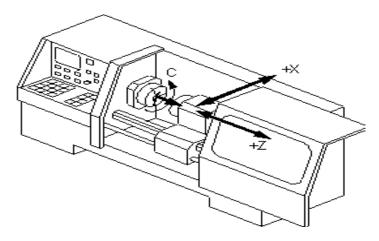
Стандартная система координат токарного станка с ЧПУ
